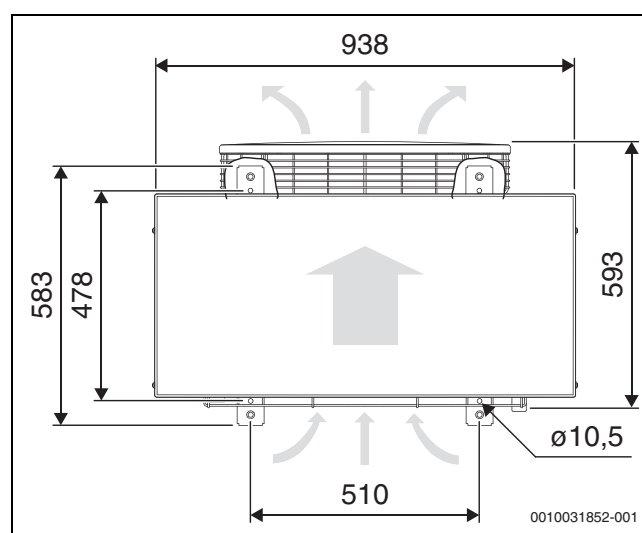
Dimensions des modèles de pompe à chaleur ODU4.2i S+ - ODU6.2i S+, vue du dessus
